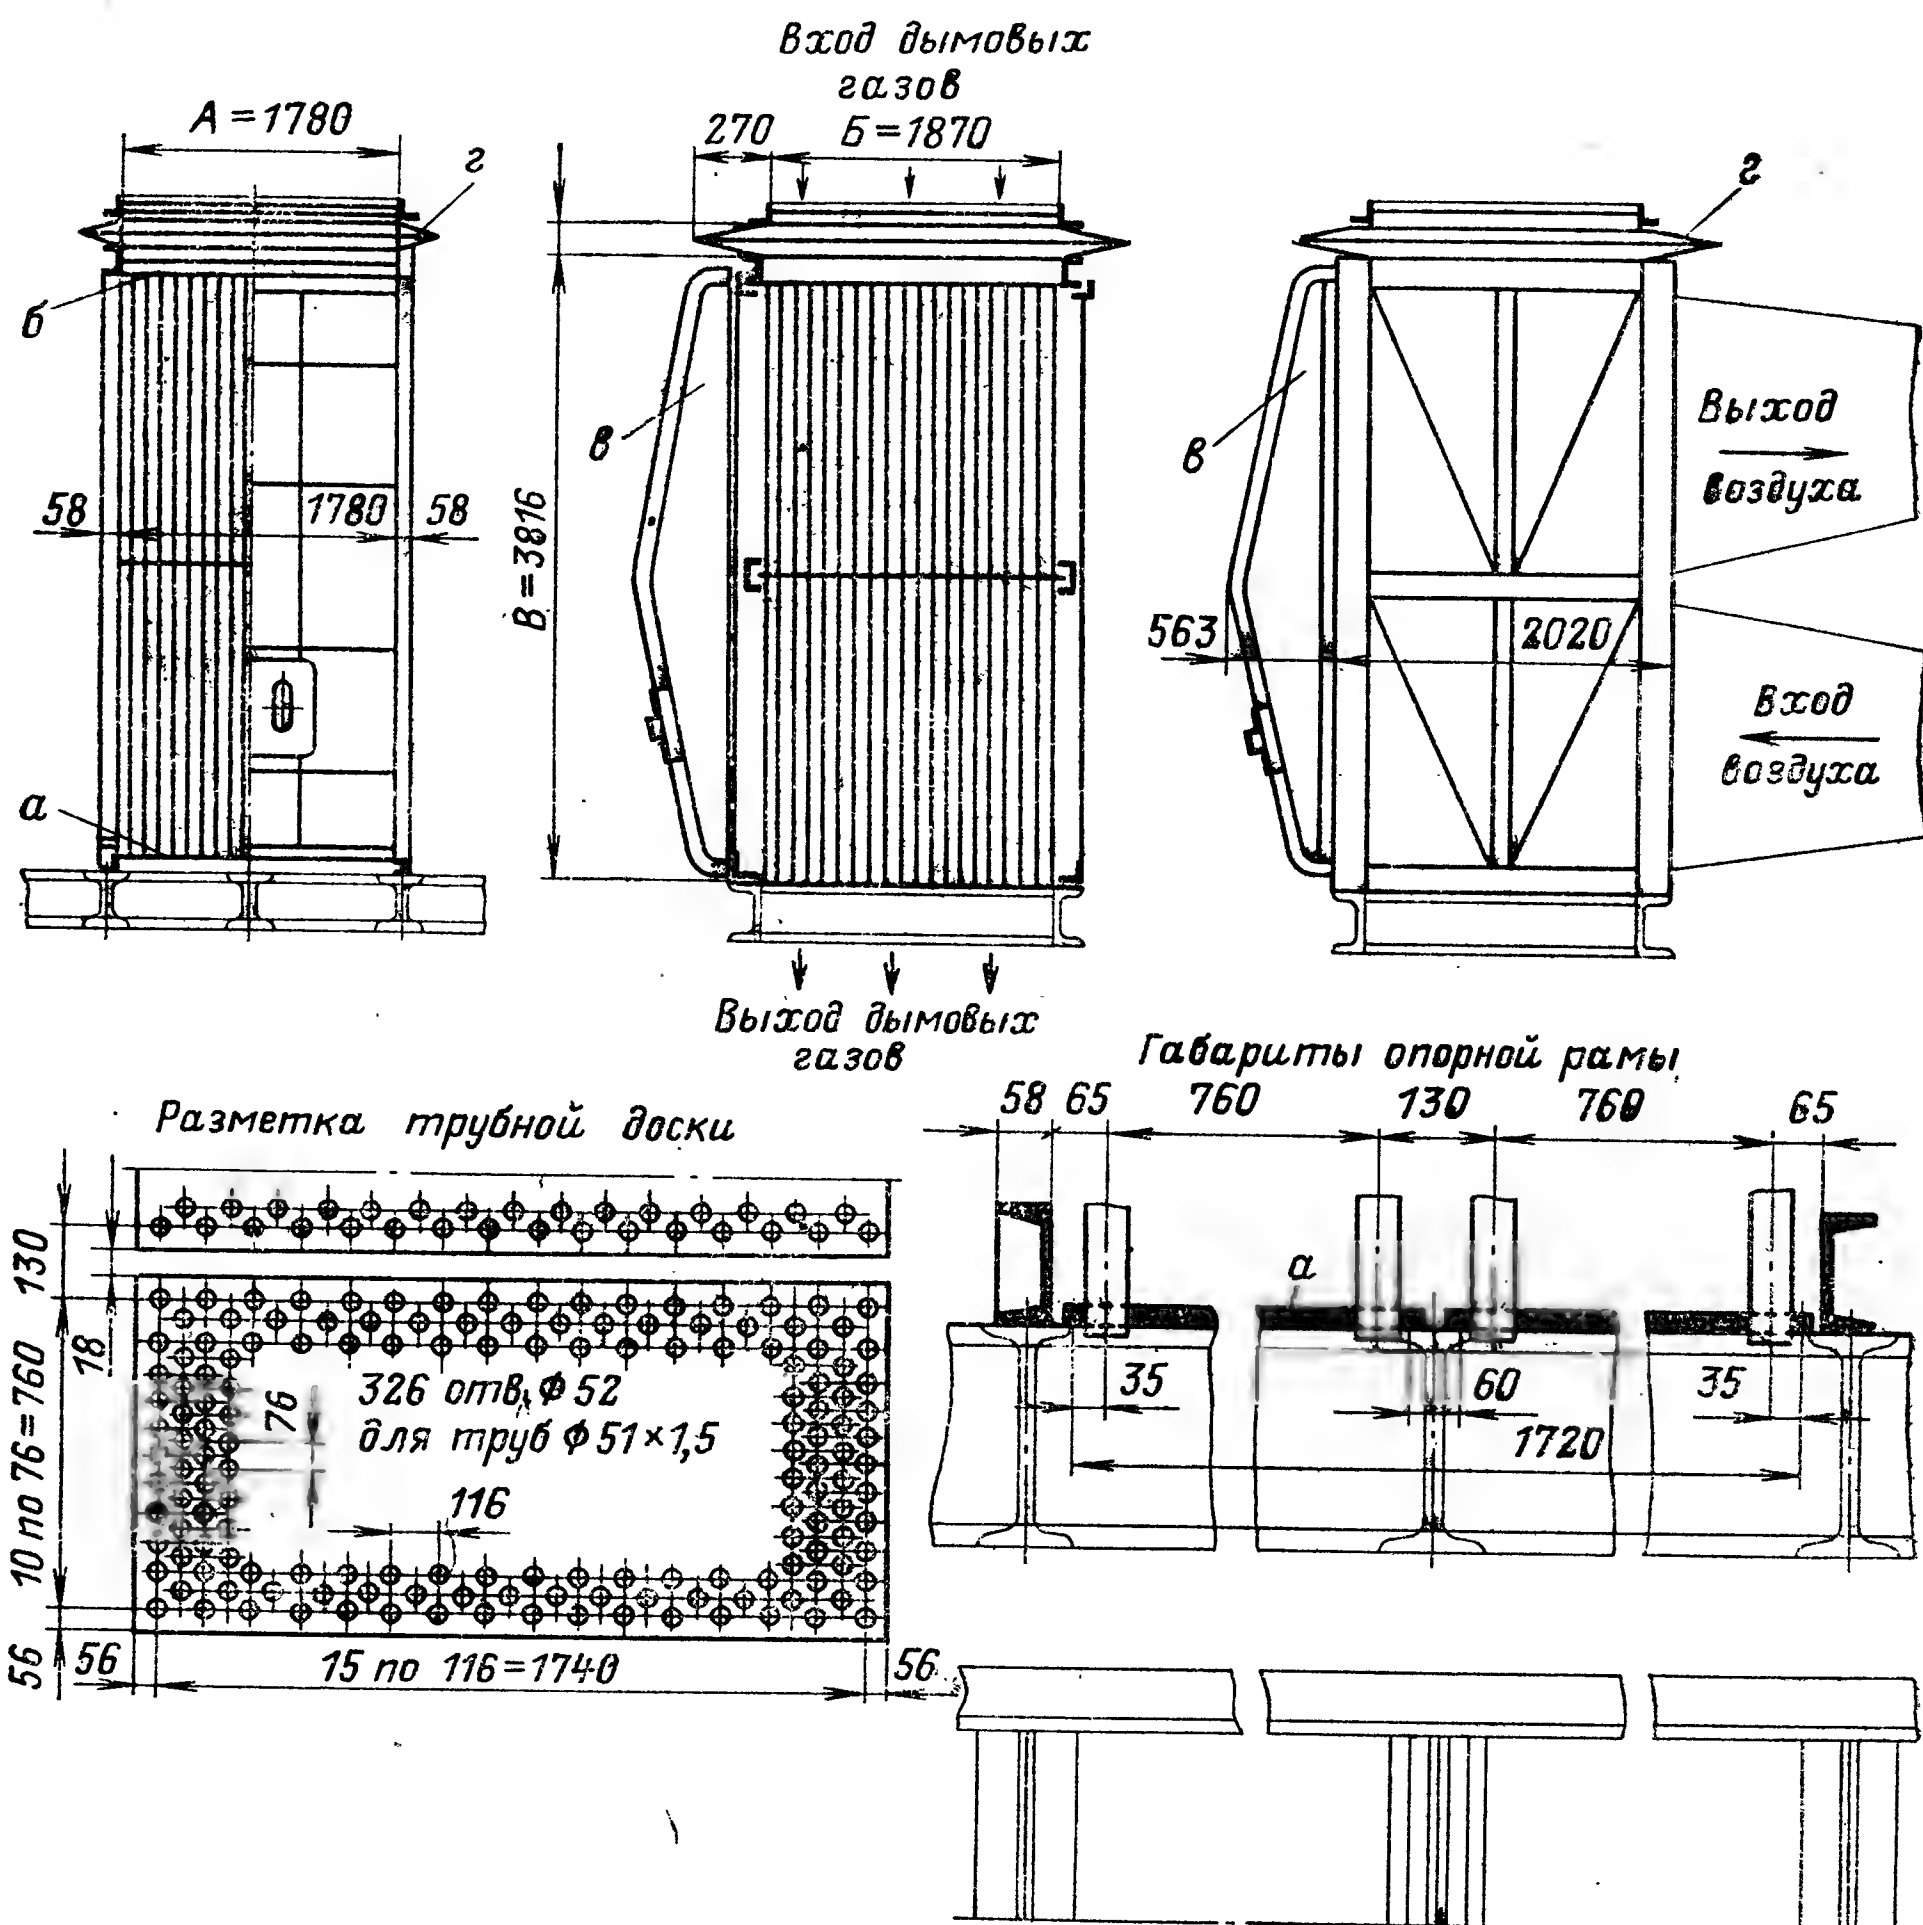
Общие виды и основные узлы стального трубчатого воздухоподогревателя.
